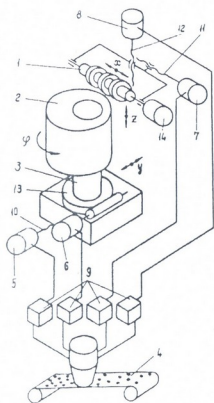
Схема нарезания некруглого цилиндрического колеса с применением ЧПУ
